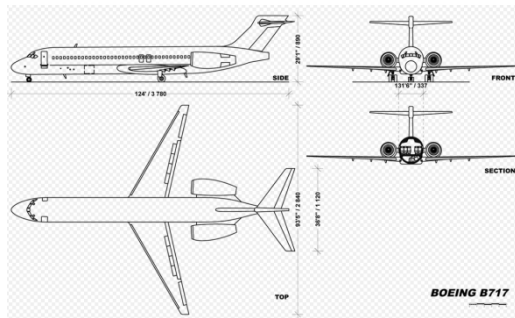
Plano de detalle e imagen del Boeing 717 (Fuente: Wikipedia)
